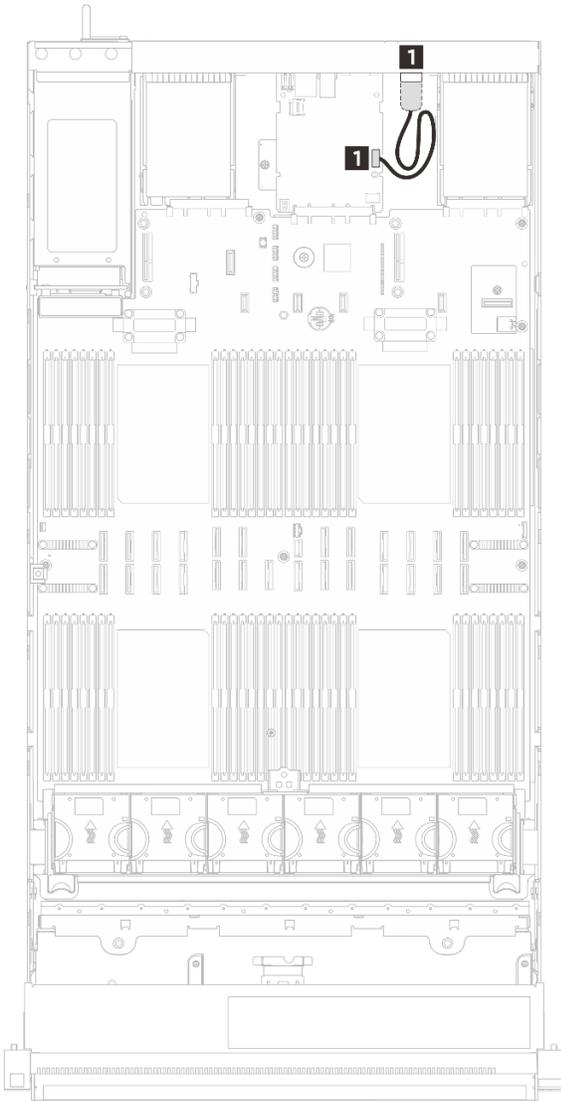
Instradamento dei cavi per il modulo della porta seriale
